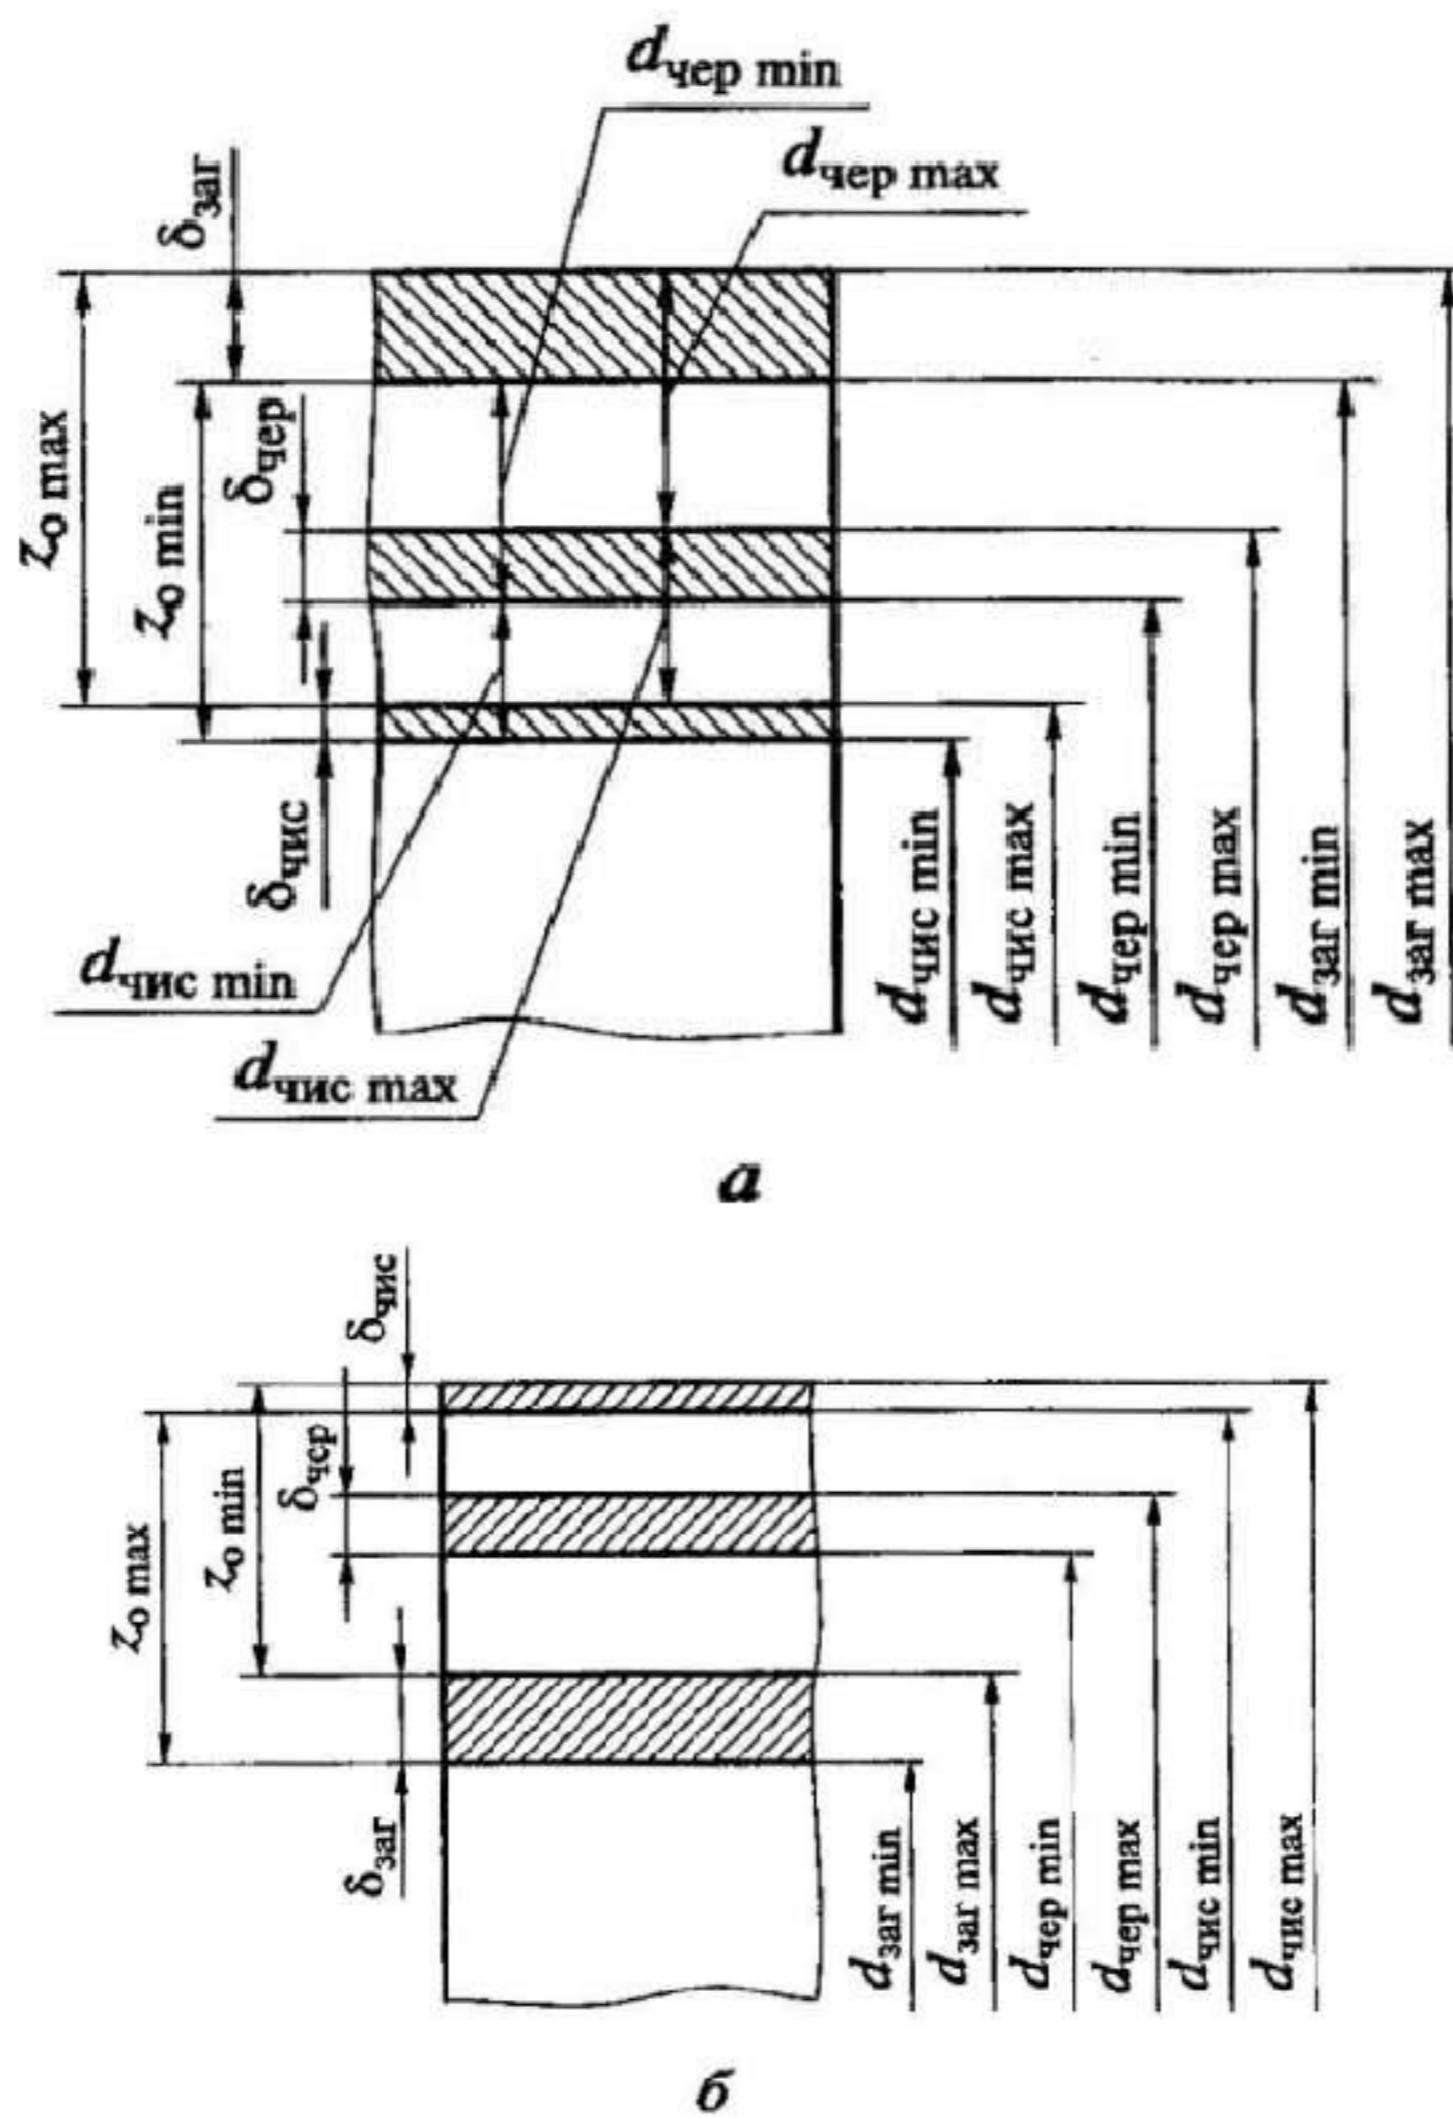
Схемы расположения предельных припусков, допусков и предельных размеров заготовки при черновой и чистовой обработке наружной (а) и внутренней (б) поверхностей вращения $z_{i \max}$ — минимальный и максимальный припуски на i -м переходе; n — число переходов.
